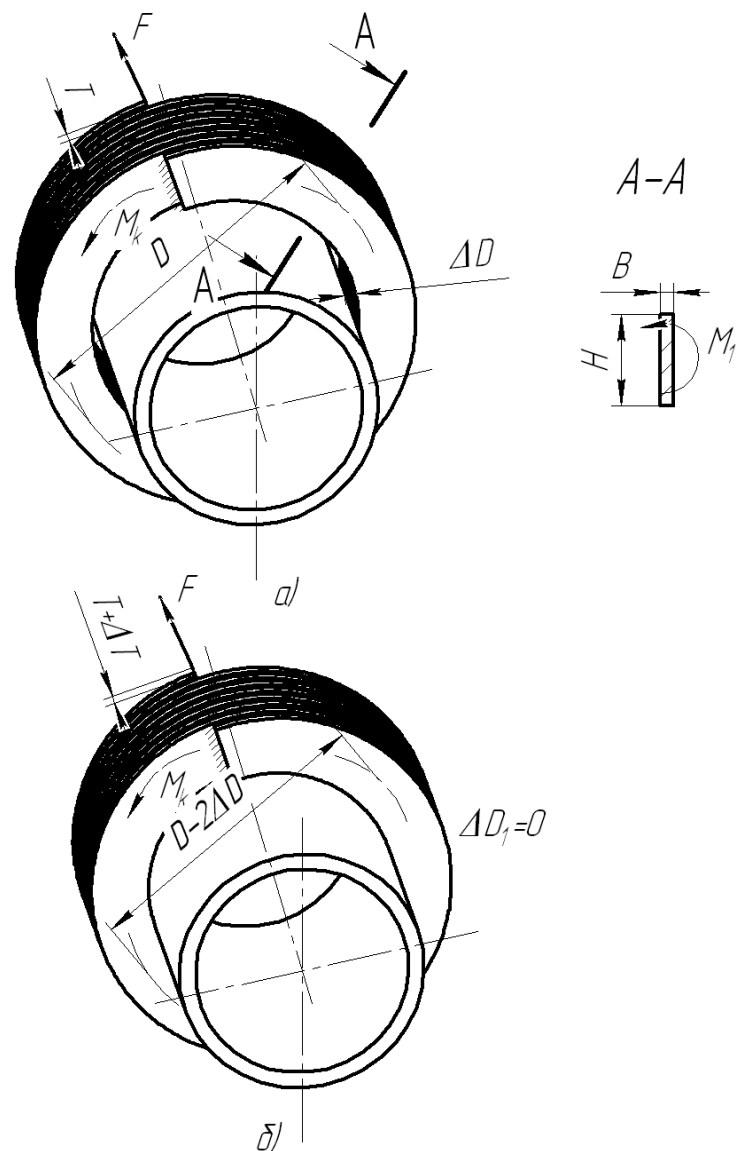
Розрахункова схема процесу затиску заготовки гвинтовим затискним елементом: а) до затиску заготовки; б) після затиску заготовки
